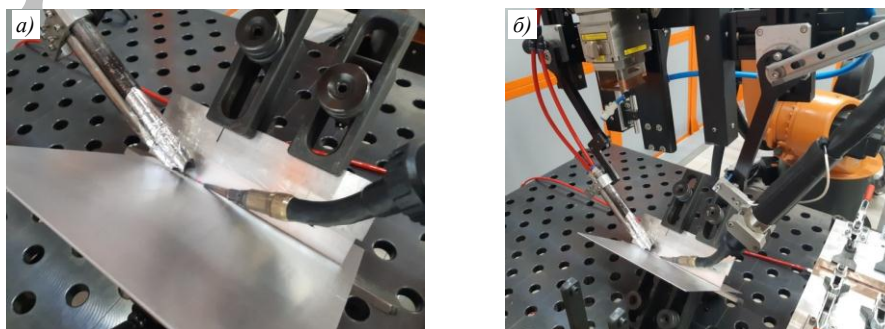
Закрепленная в оснастке заготовка (а) для проведения лазерной сварки тавровых соединений на роботизированном комплексе (б)
